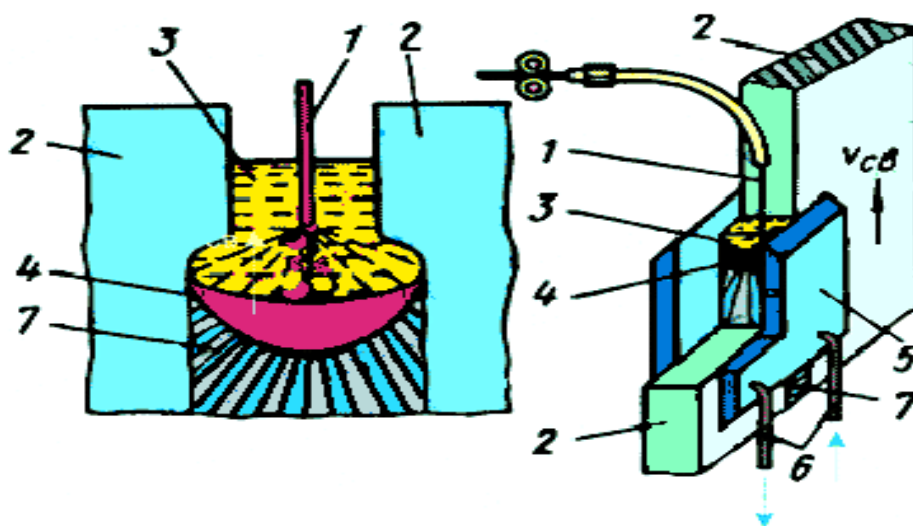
Схема процесса электрошлаковой сварки
